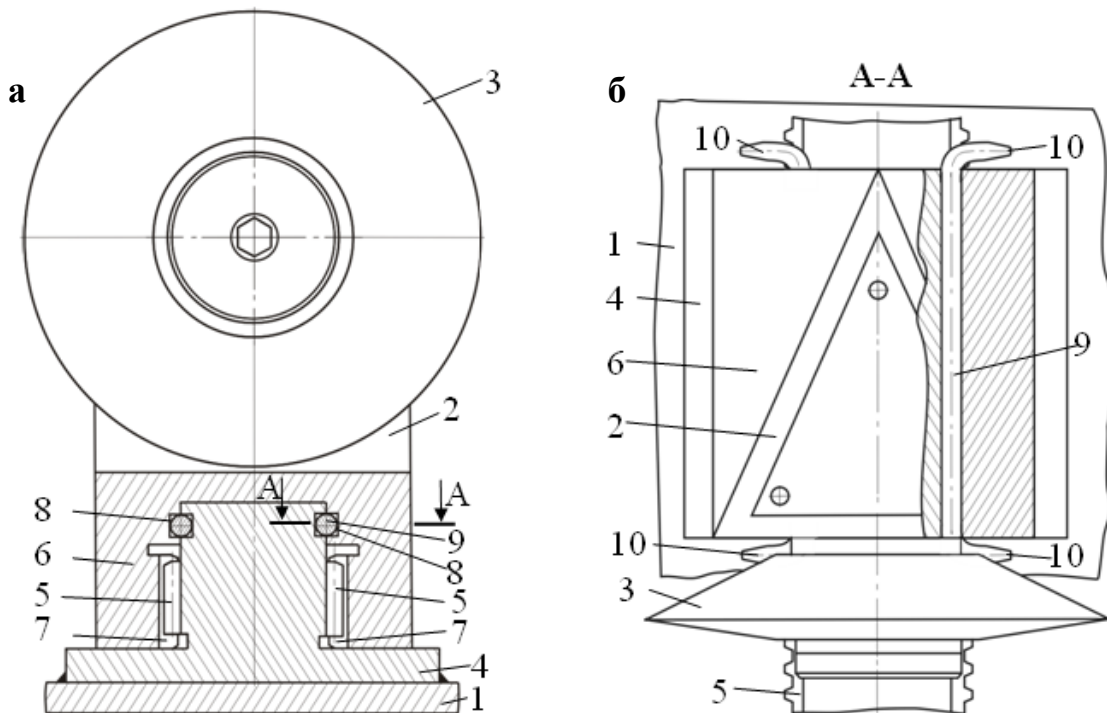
Узел крепления трехгранной призмы на пирамиде корпуса коронки: а – двухстороннее зубчатое крепление; б – проволоочный замок
